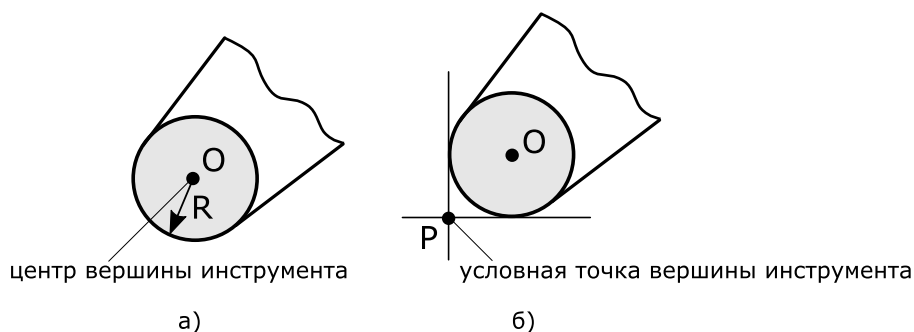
Положение центра вершины инструмента (а) и его вершины (б).
